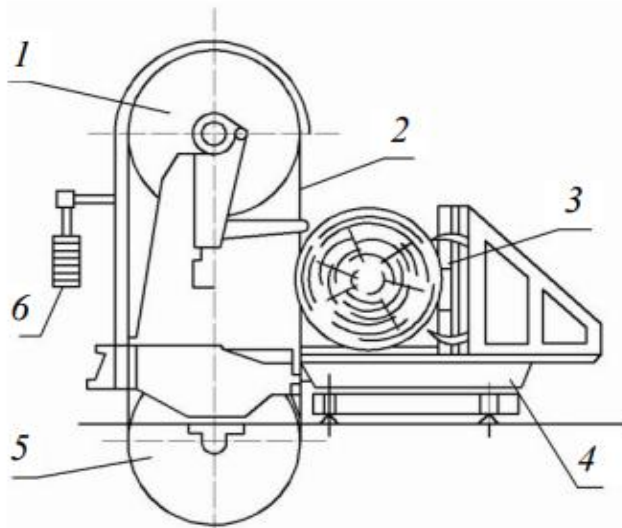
Схема пристрою стрічковопильного верстатаю
